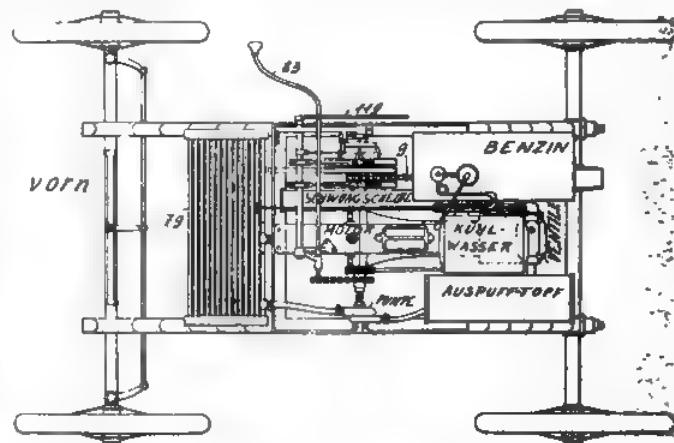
Grundriss ohne Wagenkasten.
